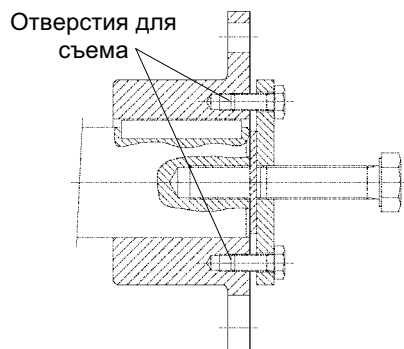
Ступица с резьбовыми отверстиями для съема
